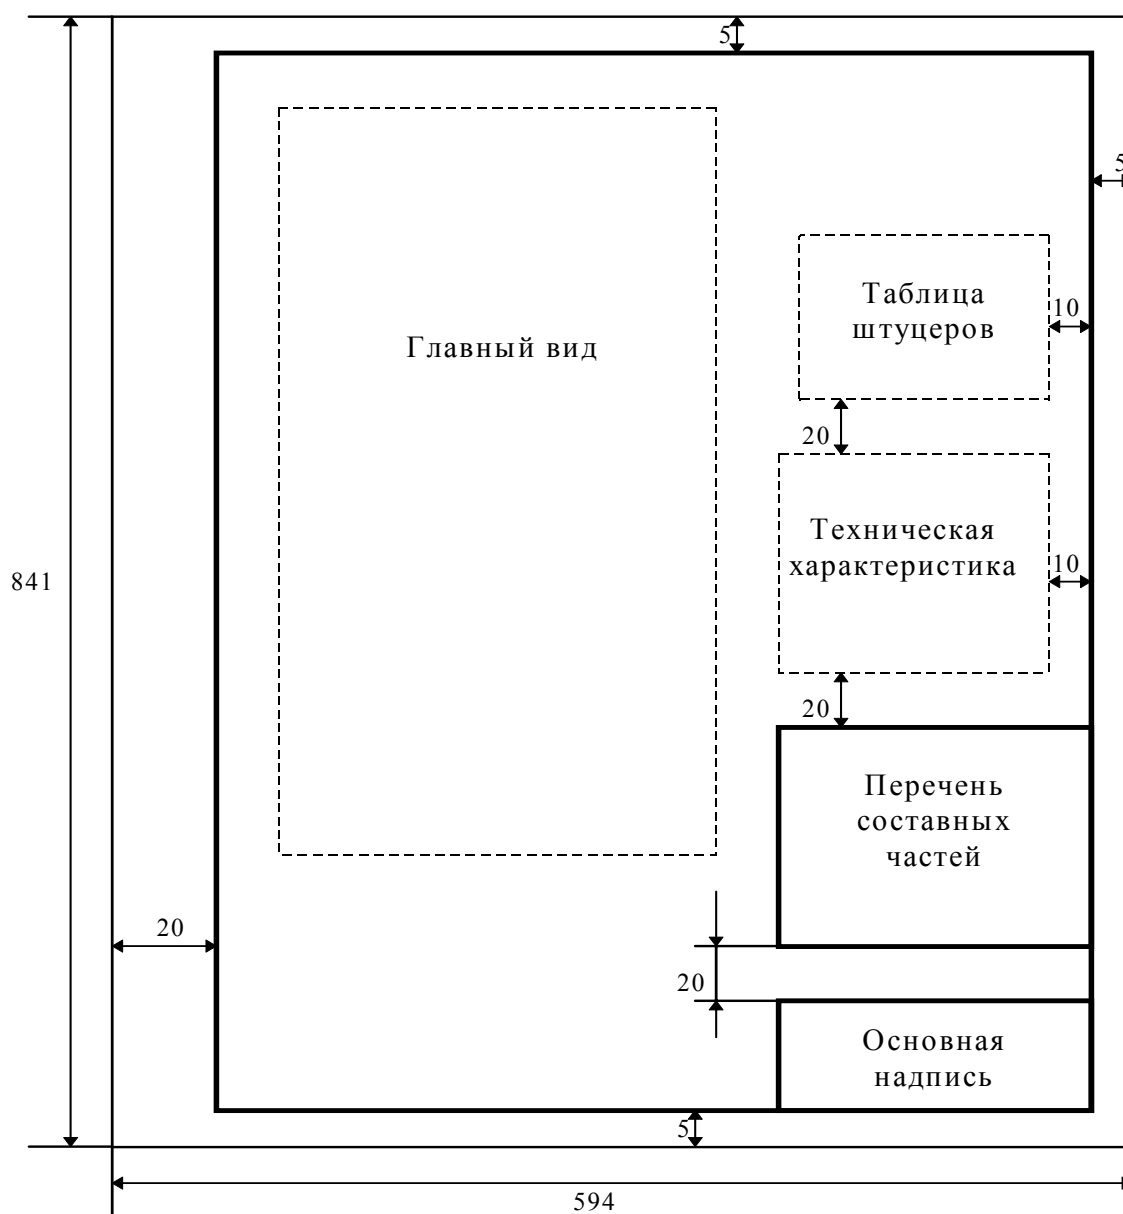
Примерное расположение элементов сборочного чертежа
